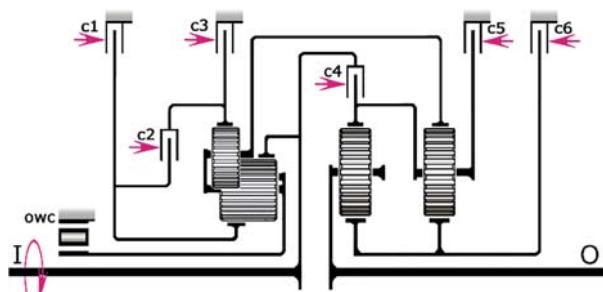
Кинематическая схема 7-ми ступенчатой планетарной коробки передач фирмы DaimlerChrysler:
